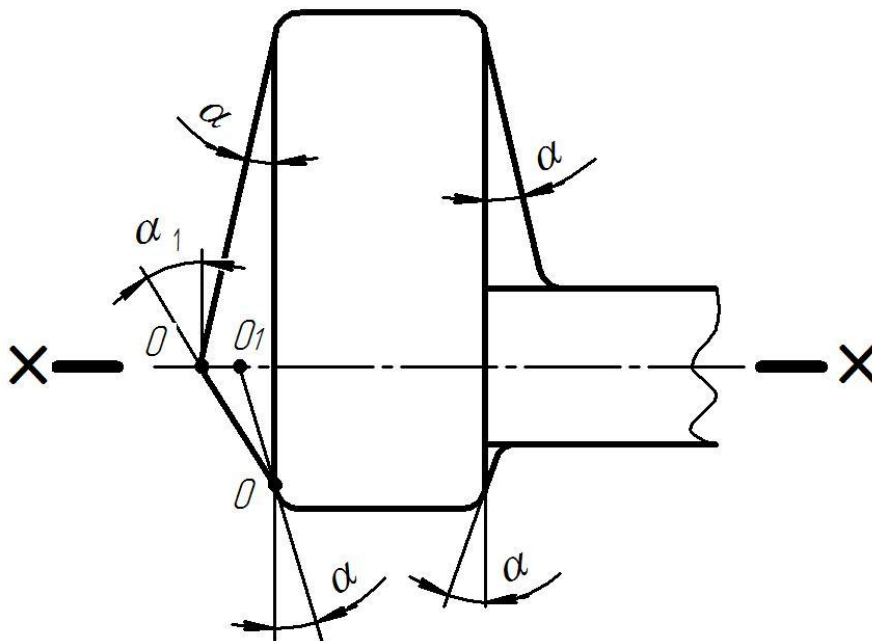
Коригування кута штампувального нахилу при несиметричному відносно поковки розташуванні поверхні різниму
